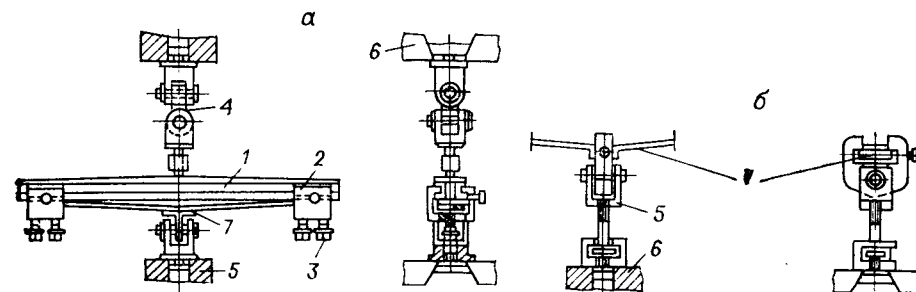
Приспособление для испытания образцов клеевых соединений на неравномерный отрыв (конструкция нижней части меняется в зависимости от образца — варианты а и б): 1 — коромысло; 2 — обойма; 3 — прижимной болт; 4 — шарнирная подвеска; 5 — нижний крепежный узел; 6 — головка испытательной машины; 7 — образцы.
